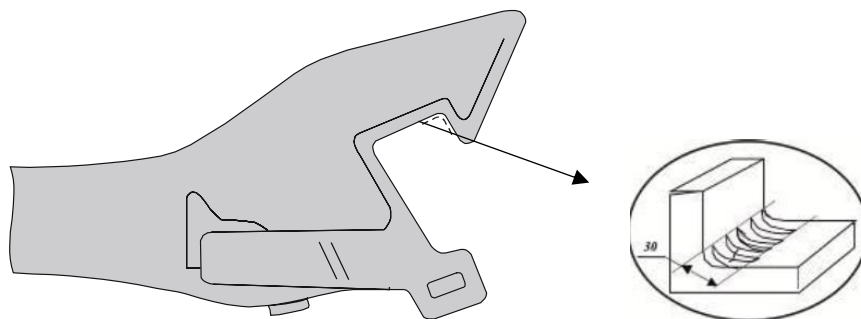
Схема сканирования угла сопряжения боковой и тяговой поверхностей большого зуба
